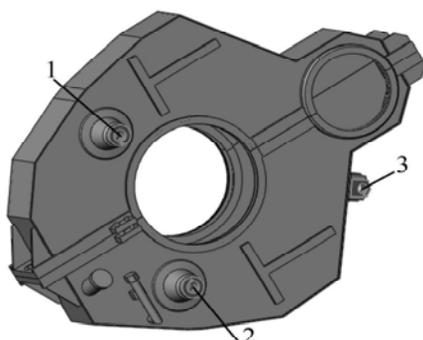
CAD модель кожуха редуктора. 1 – верхняя бобышка; 2 – нижняя бобышка; 3 – передний кронштейн.
